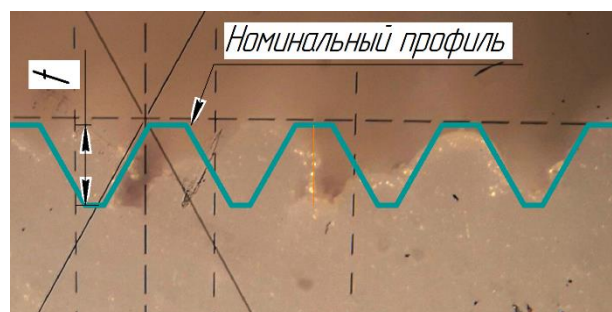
Профиль резьбы М3, сформированной в образце из PLA-пластика
